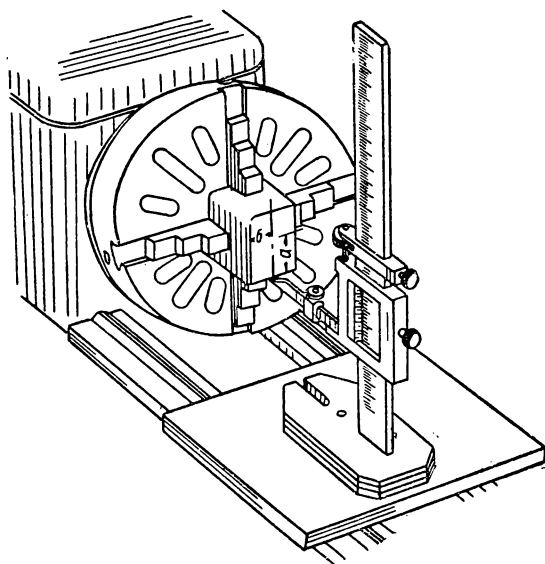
Выверка кубика при помощи штангенрейсмаса.
